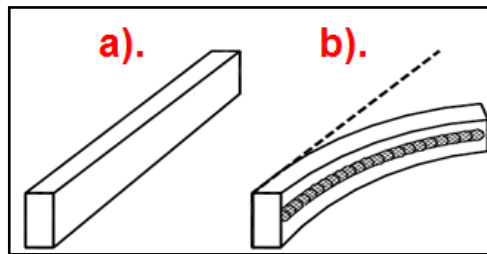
a). Ilustración de geometría de una barra antes de aplicar cordón de soldadura, b). Modificación geométrica por efecto de apilamiento, por causa de aplicar un cordón de soldadura sobre una cara de una barra de acero (2).
